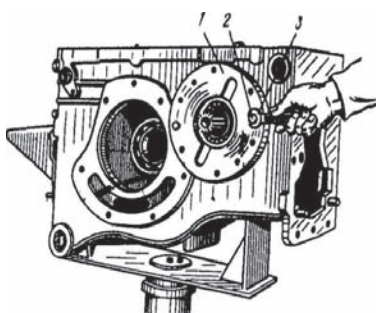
Снятие стакана подшипников в сборе с ведущей шестерней. 1 — стакан; 2 — болт; 3 — гаечный ключ.
